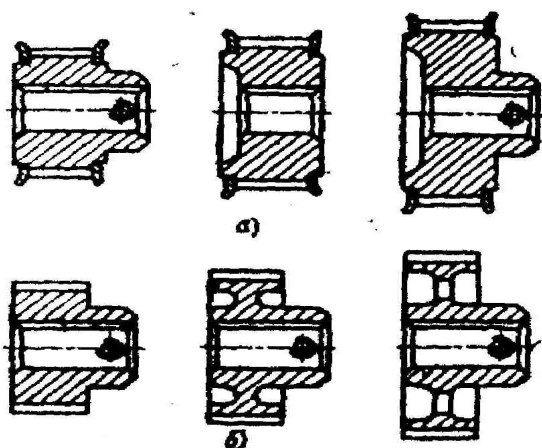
Конструкции шкивов для зубчатых ремней: а – с ребордами; б – без реборд
